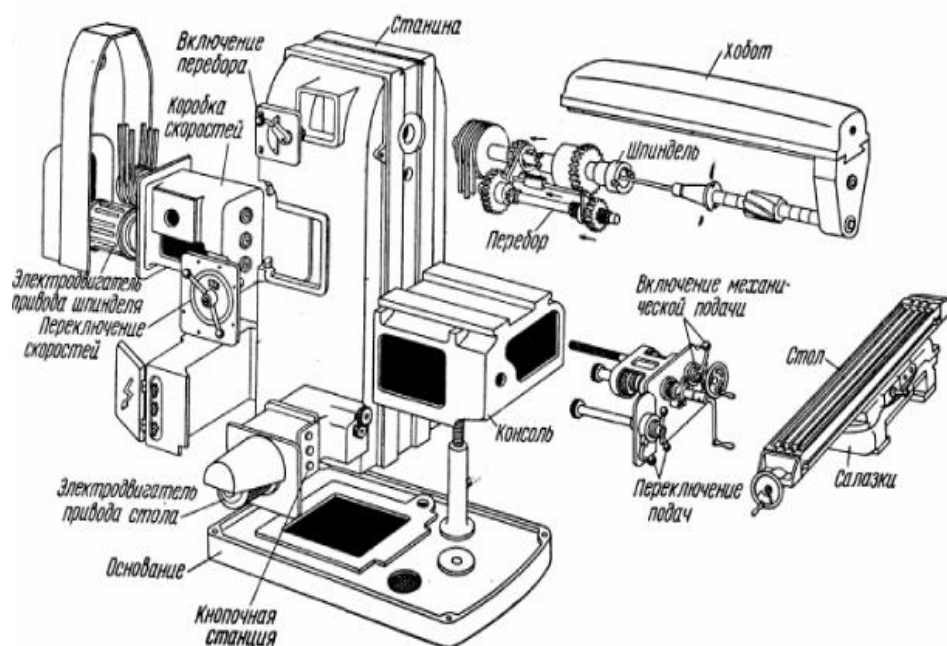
Основные узлы консольного универсально-фрезерного станка 6М82
